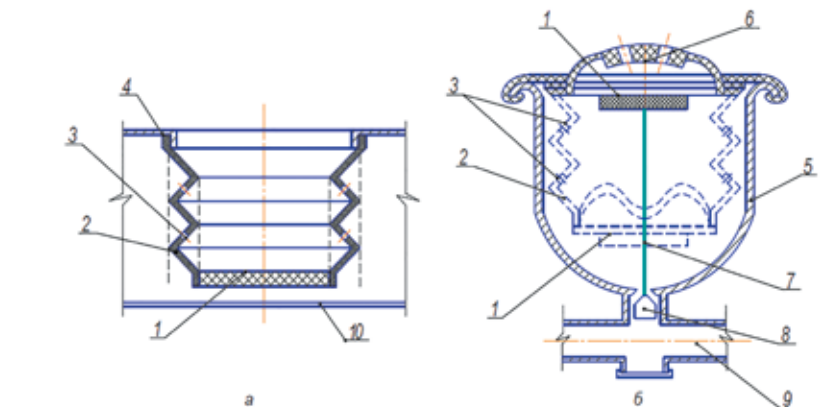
Конструктивные схемы узла забора воды животными: а – схема водопойного стакана применительно к групповой поилке; б – схема водопойного стакана – индивидуальной поилки (1 – дно водопойного стакана; 2 – стенка стакана, гофрированная; 3 – дозирующие отверстия в гофре; 4 – верхний фланец; 5 – корпус индивидуальной поилки; 6 – куполовидный колпак; 7 – поводок гибкий; 8 – клапан; 9 – рабочий трубопровод; 10 – корпус корыта групповой поилки)
